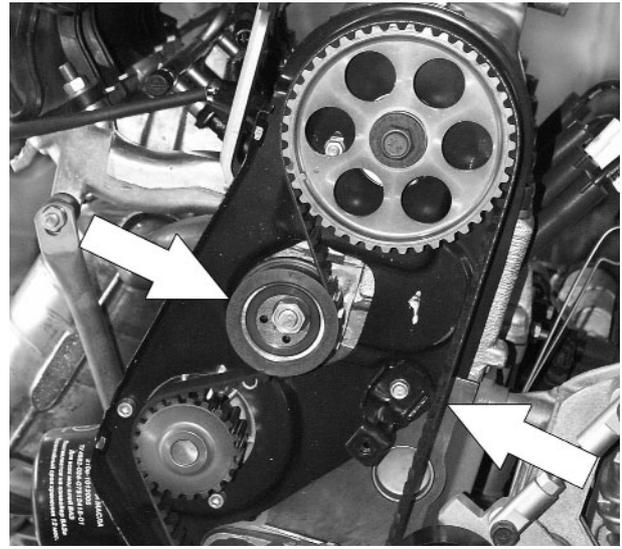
Проверка натяжения ремня привода газораспределительного механизма
